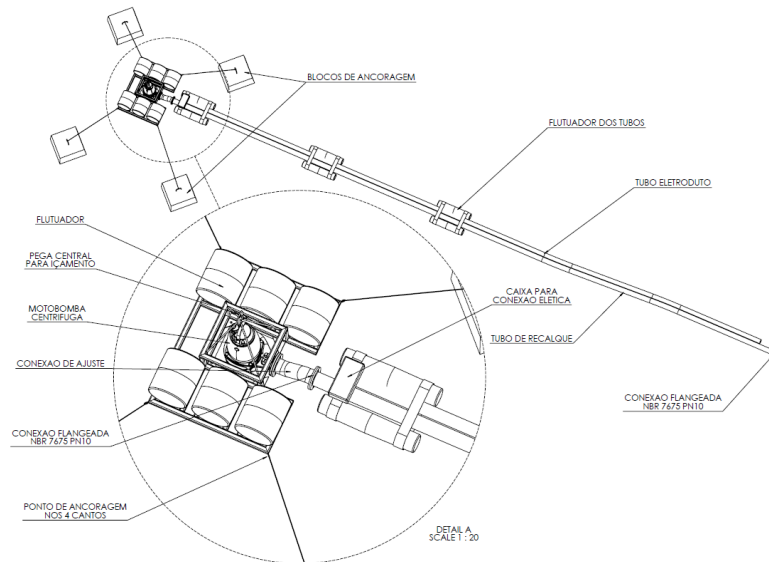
Exemplo de Conjunto Motobomba Flutuante
